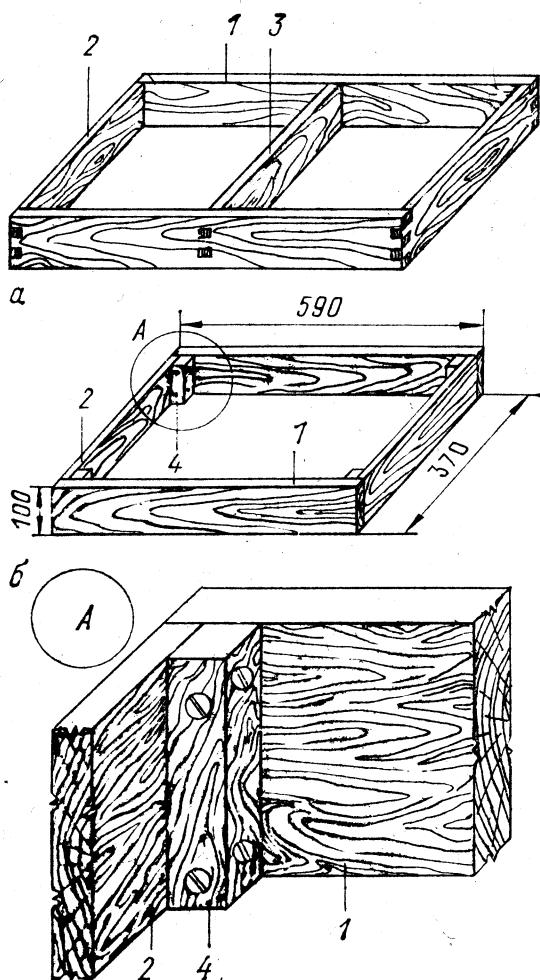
Цоколь: а — с шиповой вязкой; б — без шиповой вязки; 1 — продольная обвязка; 2 — поперечная обвязка; 3 — средник; 4 — соединительный брусок
